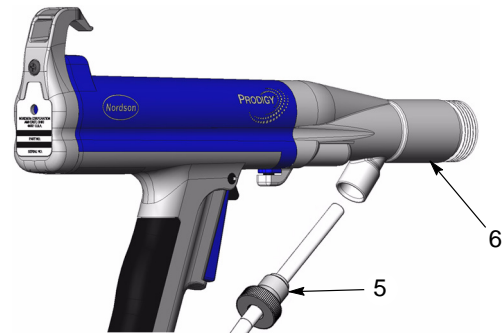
Retirer le bouton de verrouillage et le tuyau à poudre
